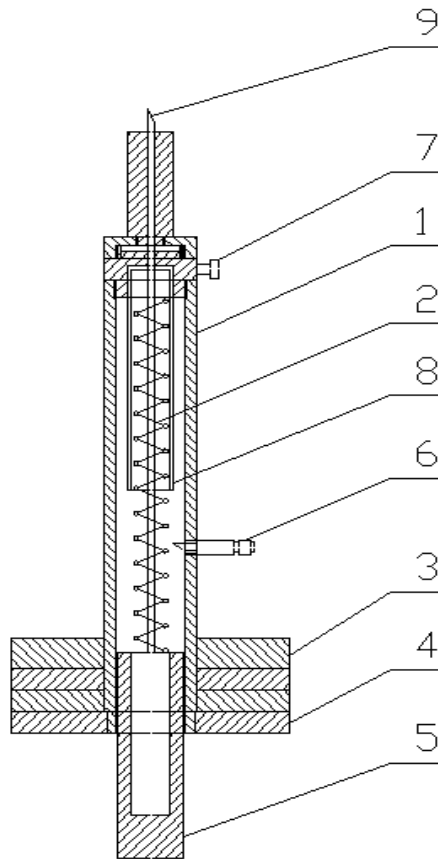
Схема пристрою ПЛС-1: 1 – корпус; 2 – пружина пуансона; 3 – допоміжні диски; 4 – опорний нижній диск; 5 – пуансон; 6 – нижній фіксатор; 7 – верхній регулятор; 8 – напрямний циліндр; 9 – напрямний шток
